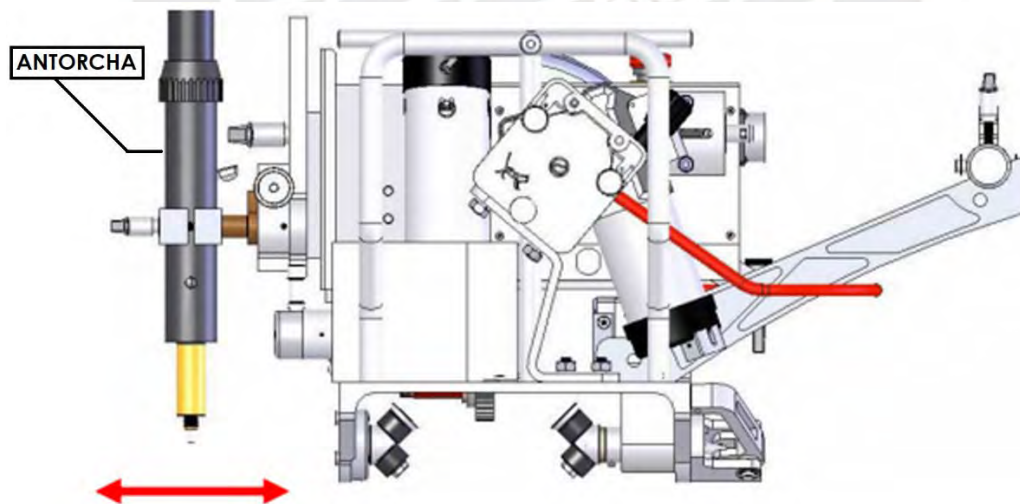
Partes de una máquina de soldadura orbital<sup>12</sup>
